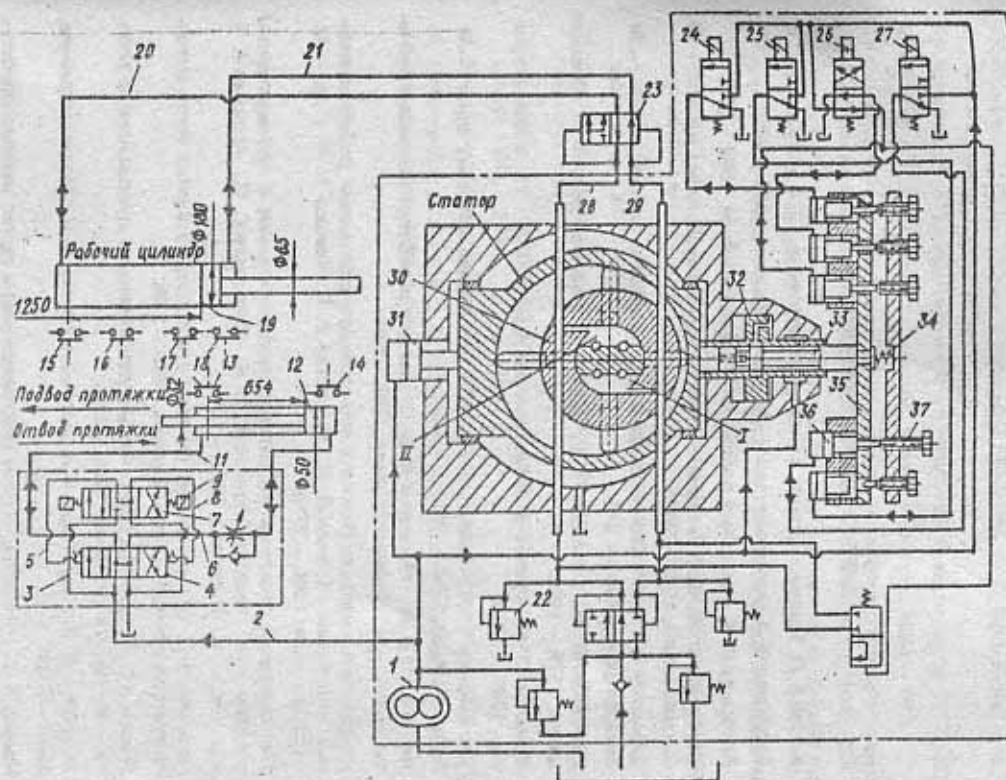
Кинематическая схема горизонтально-протяжного станка мод. 7Б55
